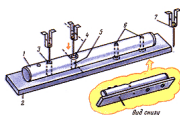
Приспособление для изготовления обоймы и готовая обойма:
